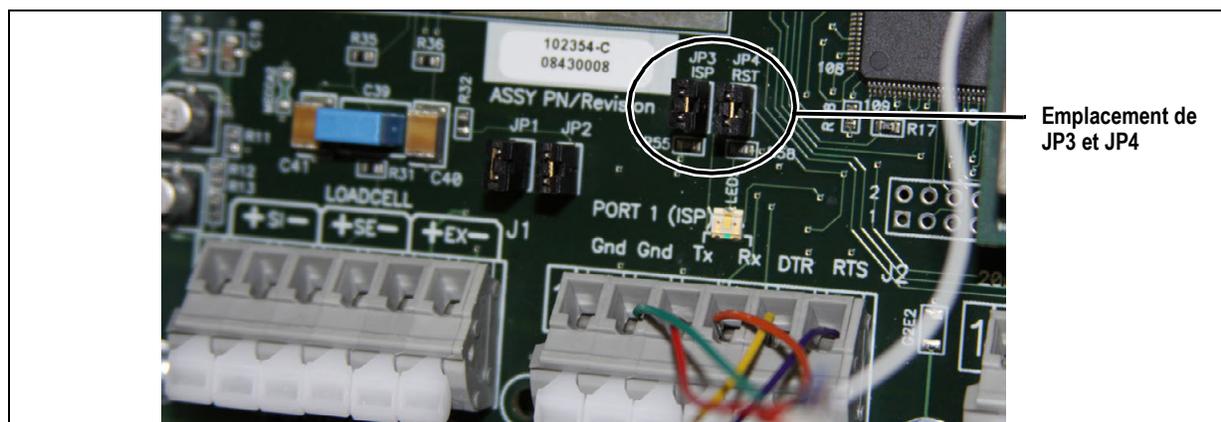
Cavaliers installés sur JP3 et JP4
